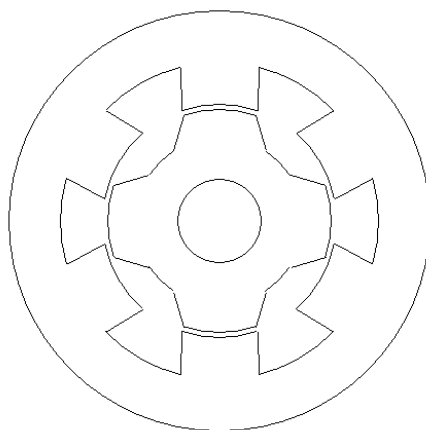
Трехфазный ВРД конструкции 6/4
